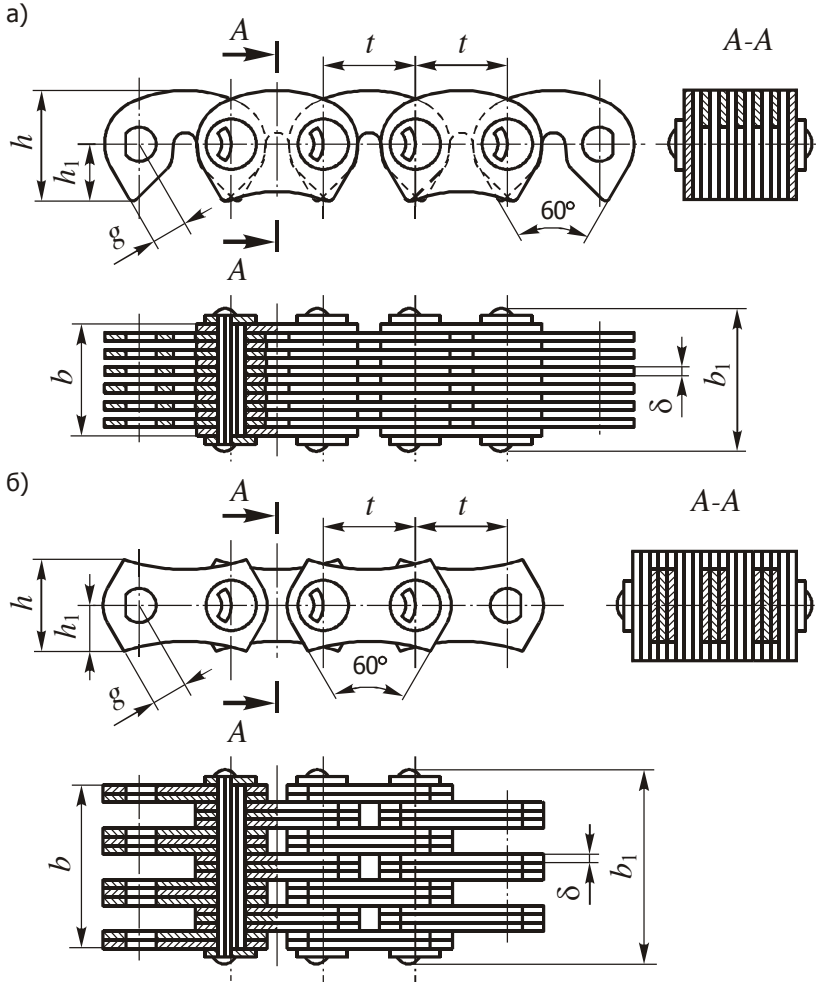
Конструкция зубчатых цепей: а – цепь типа 1; б – цепь типа 2
